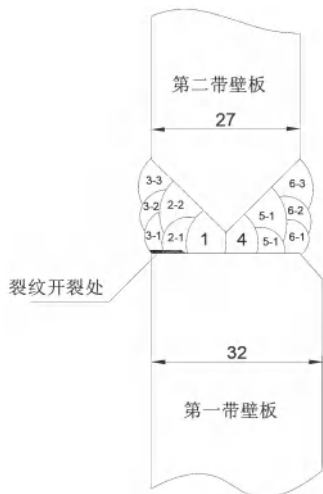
储罐 B1 环焊缝内侧裂纹出现位置
